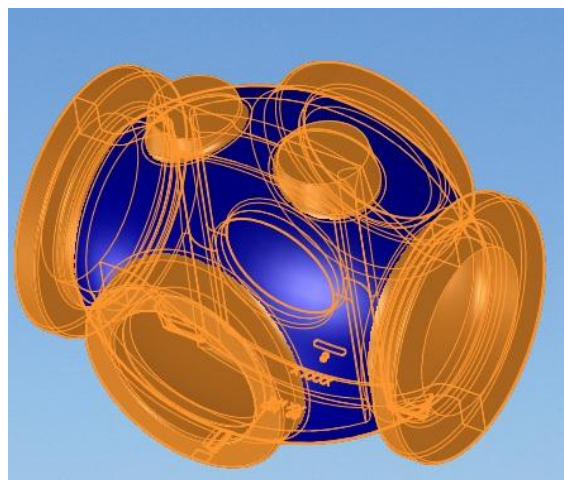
Parametry příkazu Revolved cutt (odebrání rotací)
